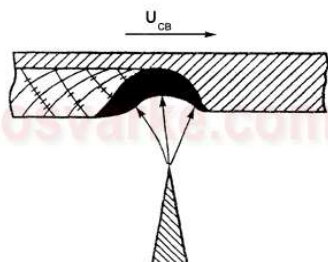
Формирование ванны и шва при ручной дуговой сварке в потолочном положении
